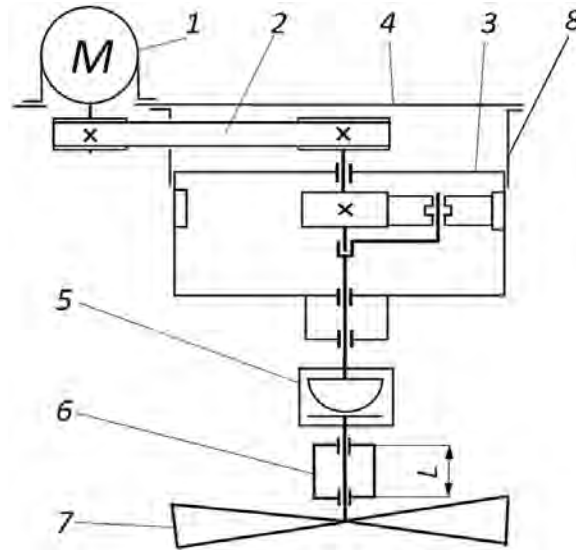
Схема привода перемешивателя раствора (фронтальный вид): 1 – асинхронный электродвигатель (фланцевое исполнение); 2 – клиноременная передача; 3 – редуктор планетарный (по схеме 2К-Н, с прямыми зубчатыми колесами, трехсателлитный); 4 – плита; 5 – муфта компенсирующая жесткая зубчатая; 6 – приводной вал с вертикальным расположением (крепление к вертикальной стойке); 7 – рабочий орган перемешивателя; 8 – переходник
